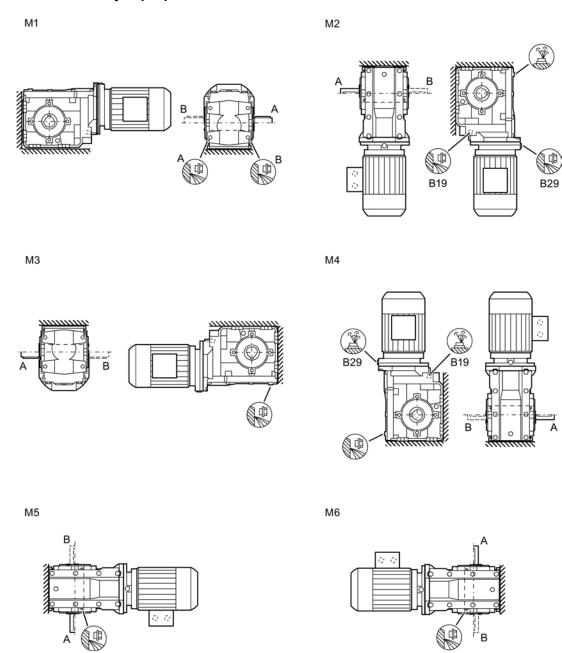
Posiciones de montaje para reductor de ejes perpendiculares B. en versión con patas, tamaños 19 - 29
